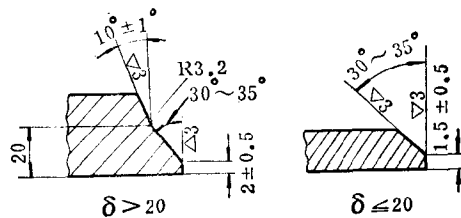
冲压焊接弯头坡口的形状与尺寸
